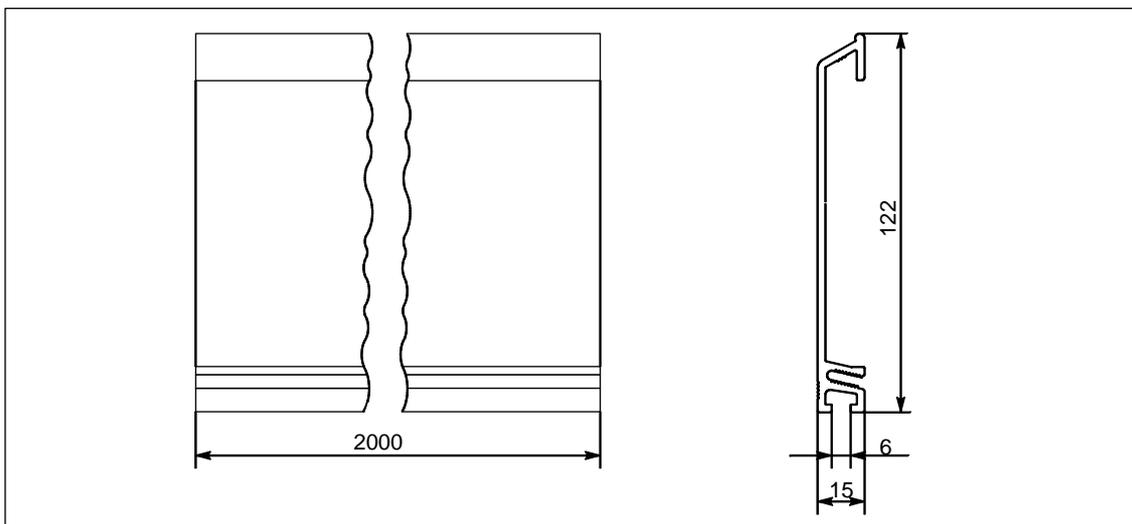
Чертеж с размерами 2000-миллиметровой профильной шины
